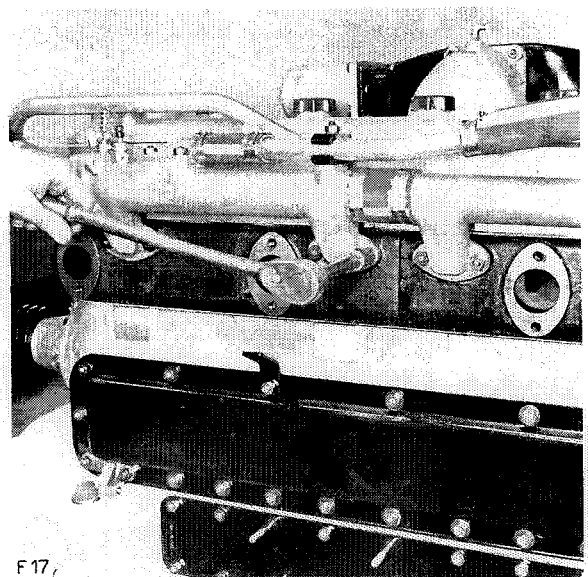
Lösen der Muttern auf den Stiftschrauben zur Befestigung der Anschlussflansche
